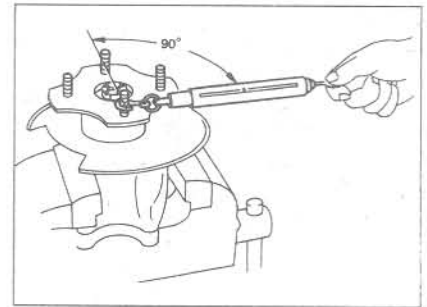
Проверка крутящего момента переднего подшипника ступицы на стойке колеса (Глава 4)
